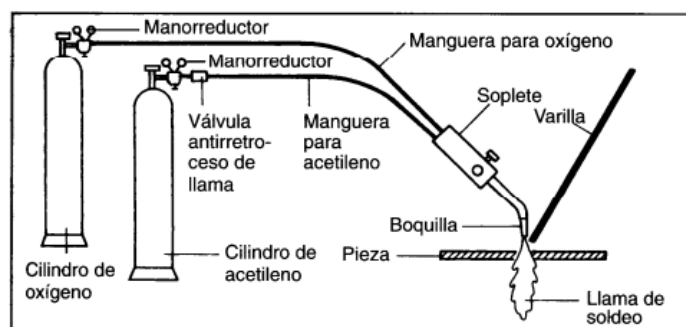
Equip de soldadura Oxiacetilènica. Apunts Tecnologia Mecànica.
